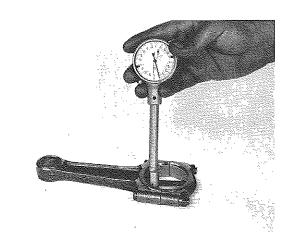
Controllare il gioco radiale Checking radial clearance
